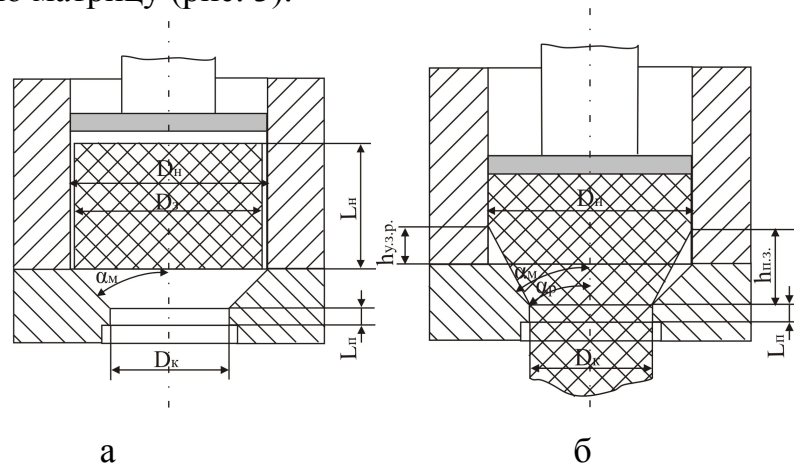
Прессование с прямым истечением сплошного профиля из круглой заготовки через одноканальную матрицу на стадии распрессовки (а) и на стадии начала истечения металла (б)
